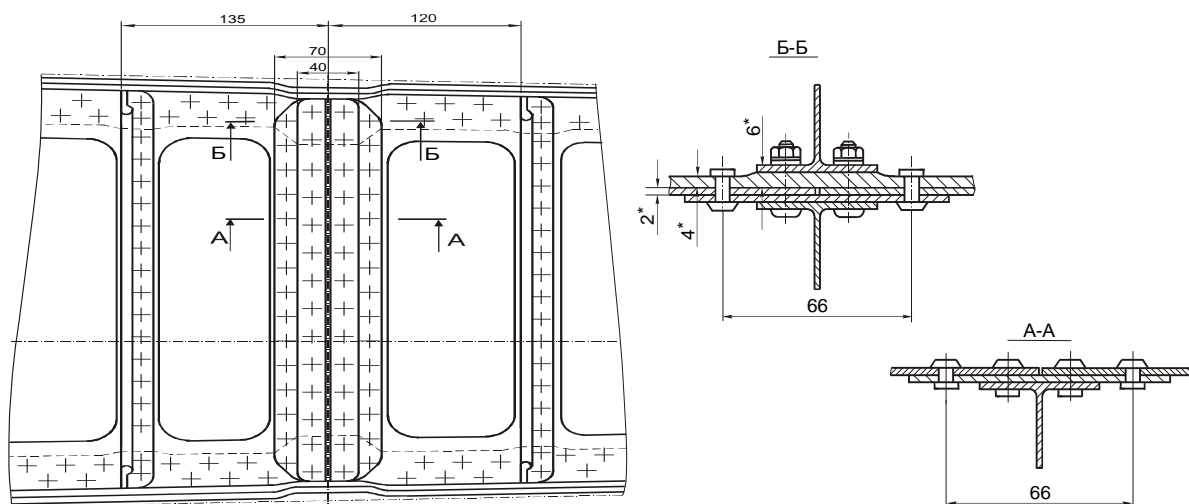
Фрагмент сборочного чертежа сборочного лонжерона в зоне поперечного стыка стенок
